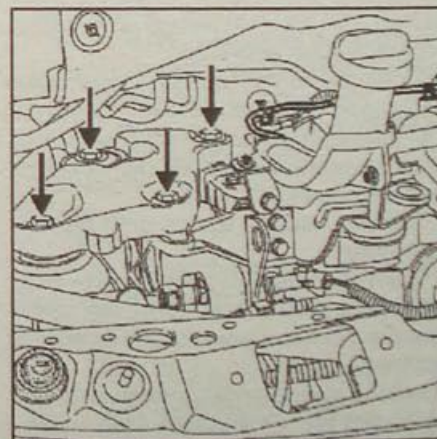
Расположение болтов крепления правой маятниковой подвески двигателя
